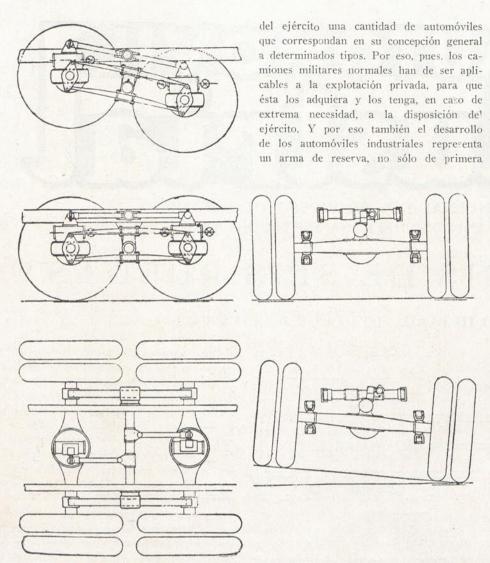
Montaje del tren zaguero en los chasis W. D.
